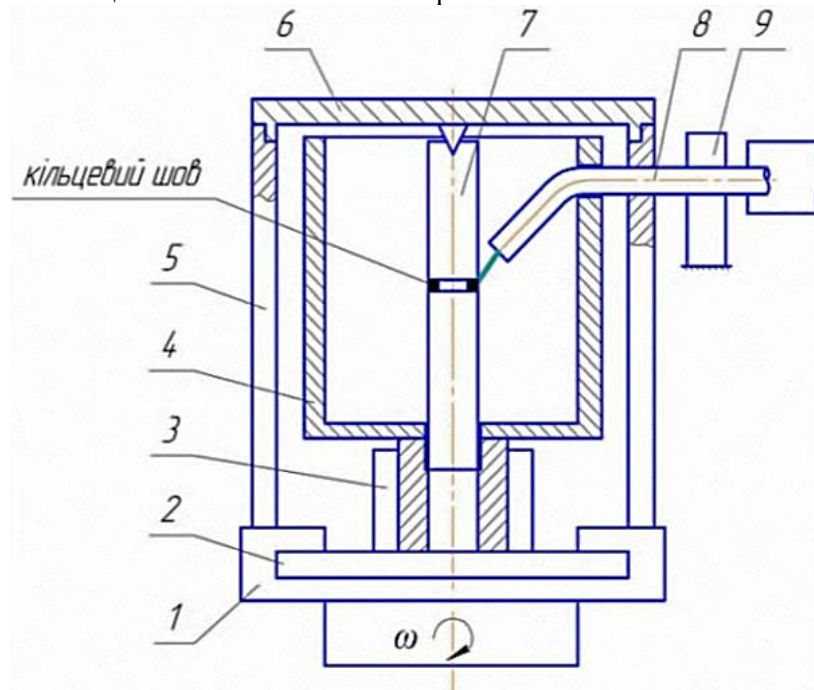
Пристрій базування та закріплення циліндричного зразка для кругового заплавлення кільцевої канавки на модернізованому автоматі А-825М: 1 – стояк приводу; 2 – поворотний столик; 3 – трикулачковий патрон; 4 – кожух захисний; 5 – циліндричний стакан; 6 – кришка; 7 – зразок-заготовка; 8 – мундштук зі шлангом; 9 – стійка для мундштука автомата.
